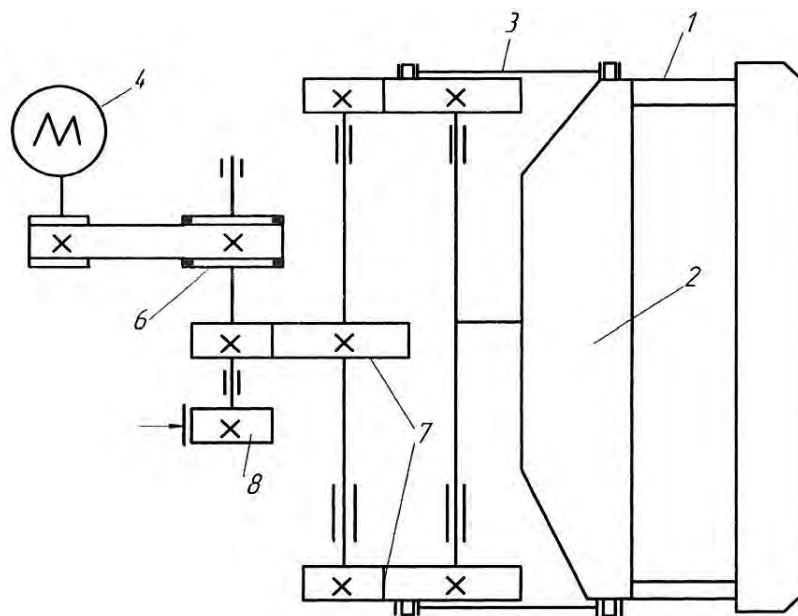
Кинематическая схема листогибочного пресса
